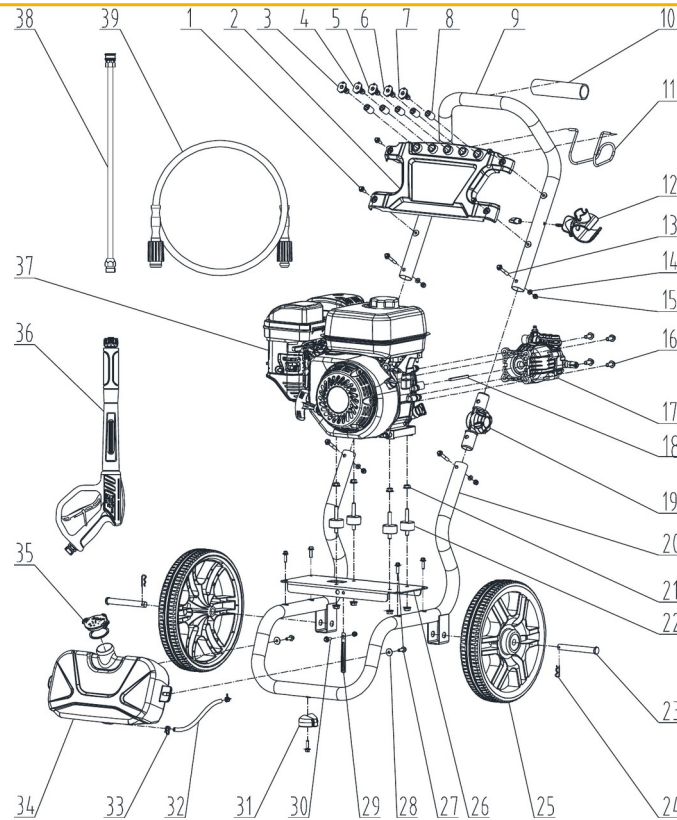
Vista explodida do AY-210 KT (ref. 5419960)
